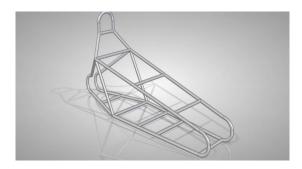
Desenho 3D do Chassi em SOLID EDGE
